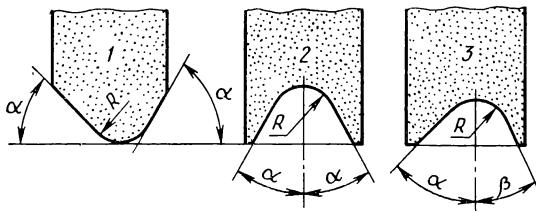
Профили кругов, образованные дугами и касательными к ним
